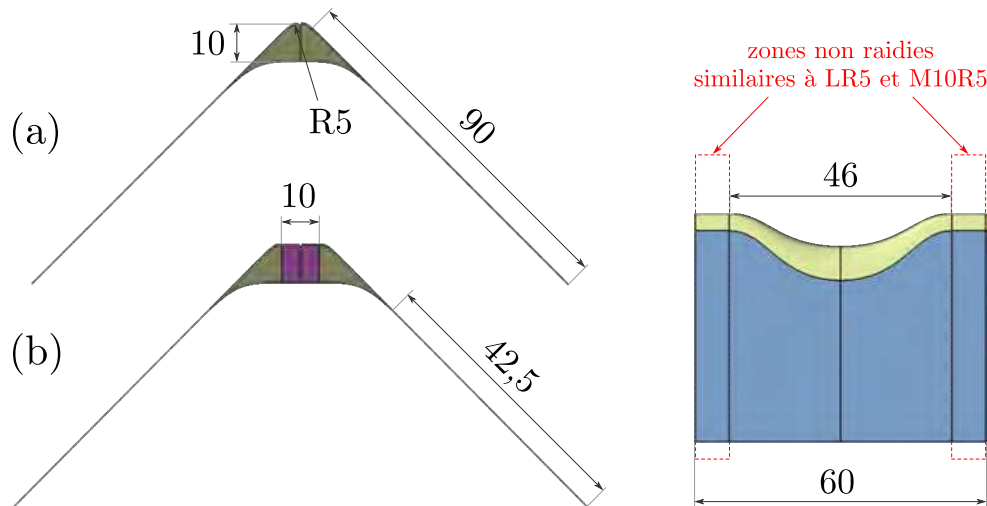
Principales dimensions (en mm) des pièces LR5S (a) et M10R5S (b)
